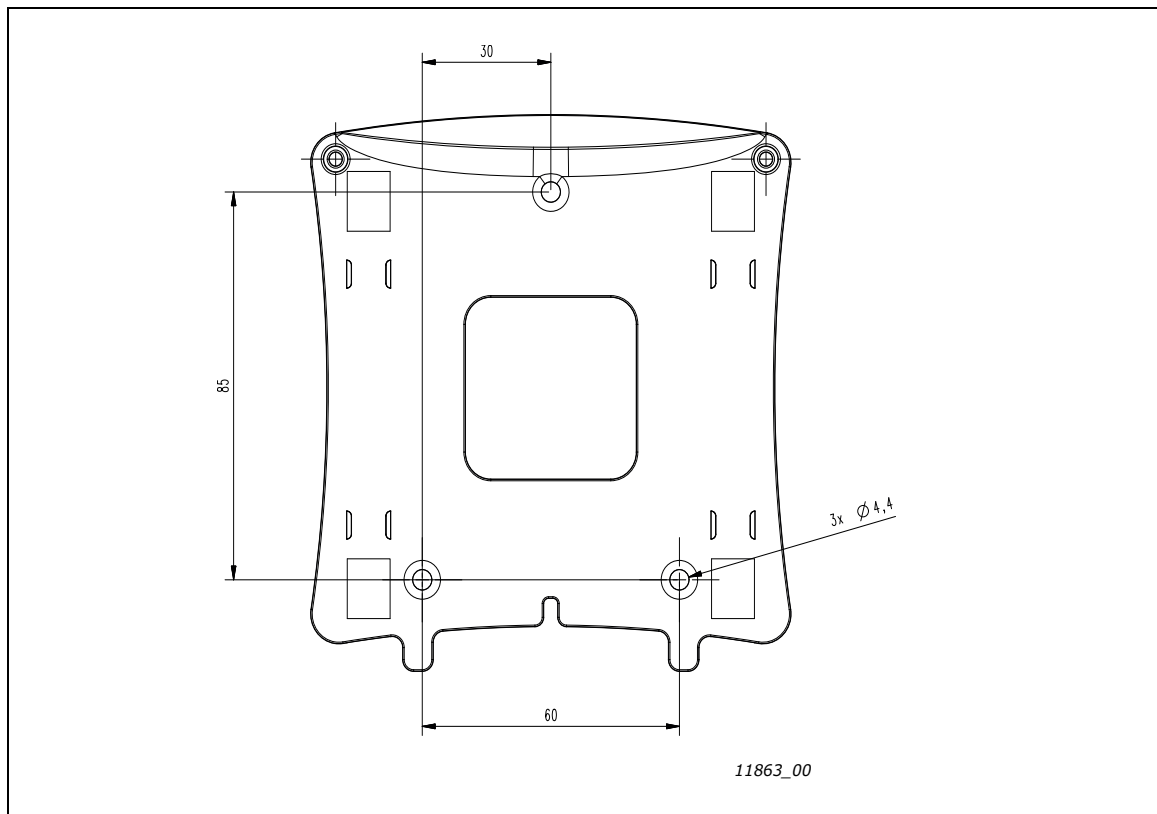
Dimensiones del soporte de pantalla para montaje en pared.
